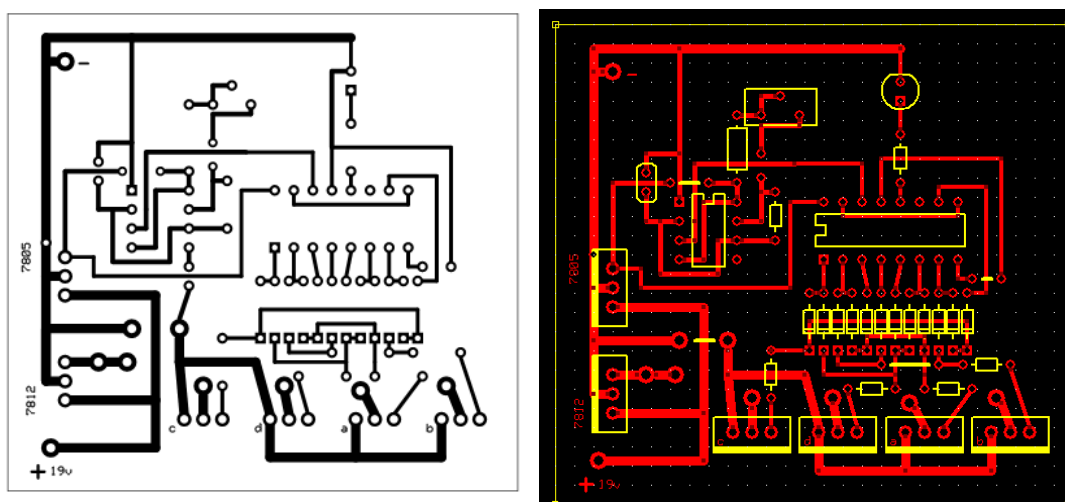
Desenho da placa de circuito impresso do controle do motor.
